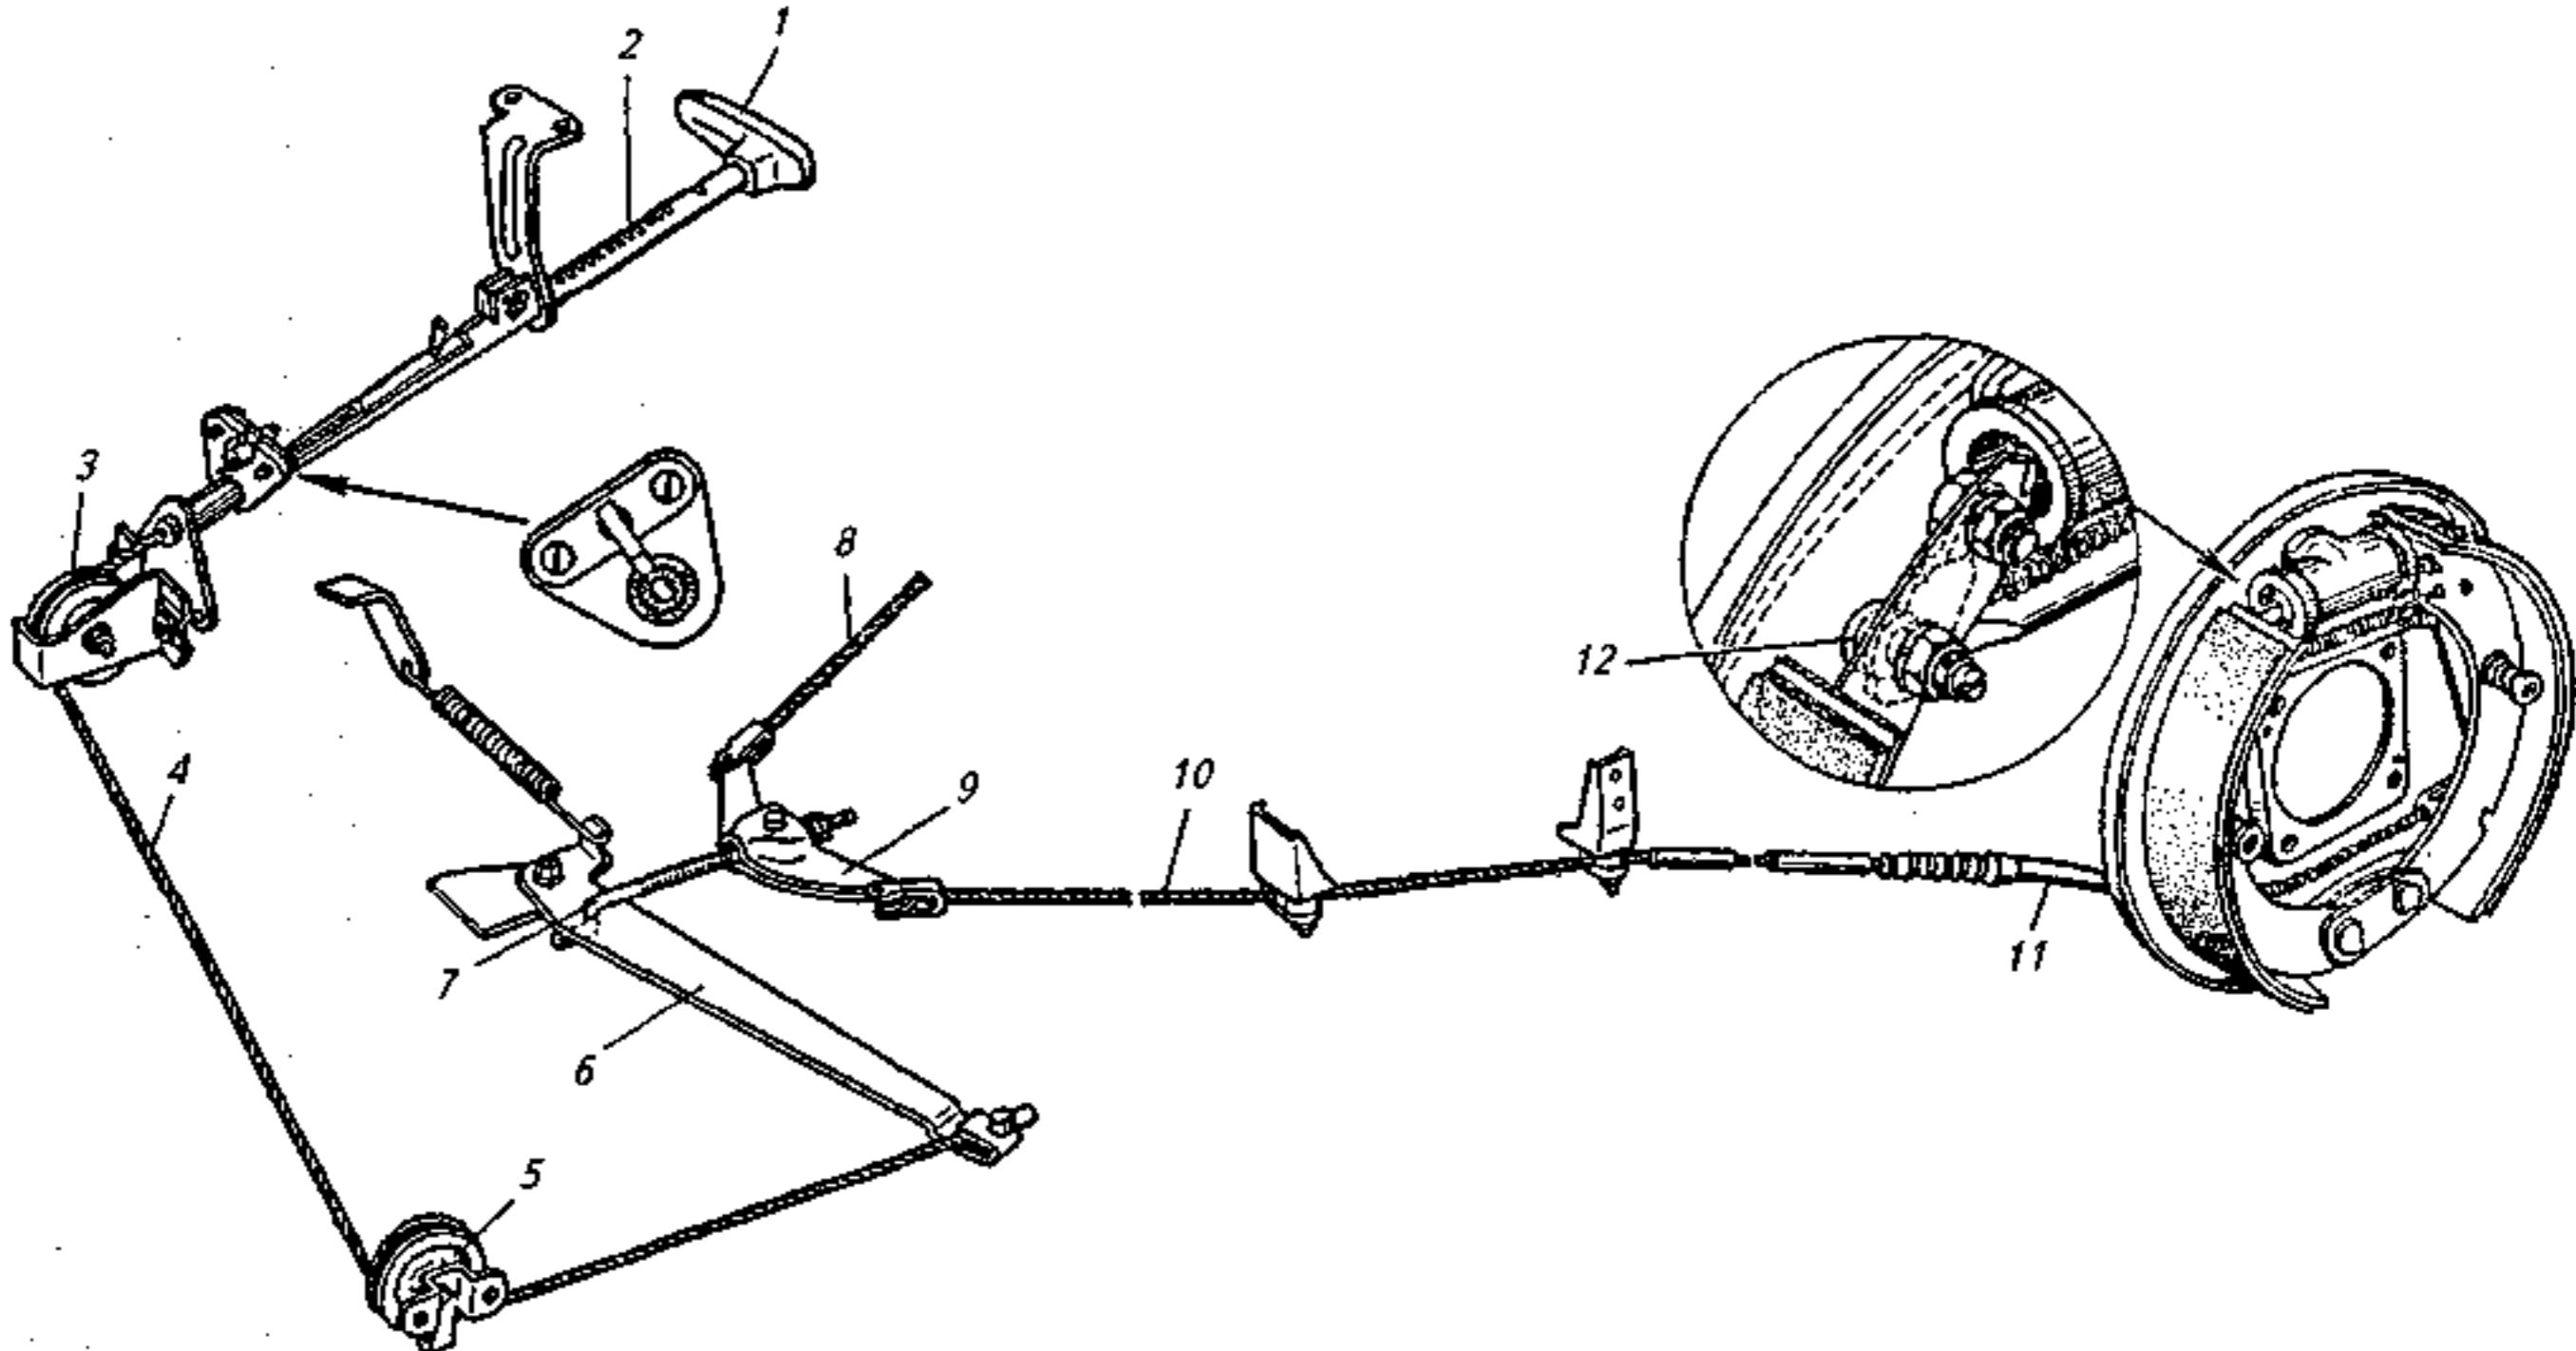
Стояночный тормоз, действующий на задние колеса: 1 – рукоятка; 2 – рычаг; 3,5 – ролики троса; 4 – передний трос; 6 – промежуточный рычаг; 7 – стержень; 8,10 – тросы привода тормозных механизмов; 9 – уравнитель тормоза; 11 – трубка; 12 – эксцентриковая ось разжимного рычага
